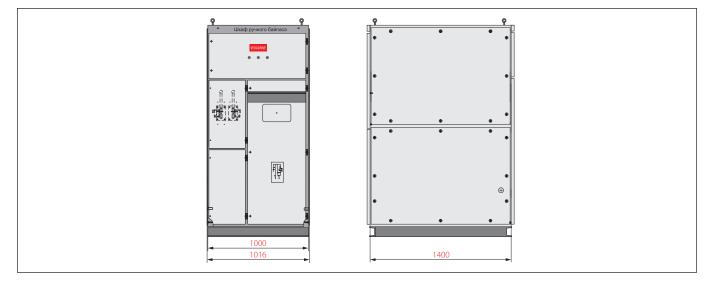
Корпус шкафа ручного байпаса типоразмера МВ03
